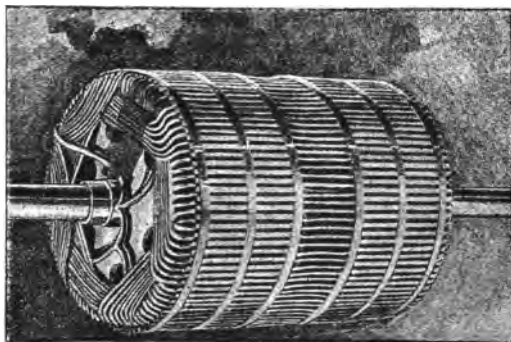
Vue des inducts enroulés de la Stanley Electric Co.
